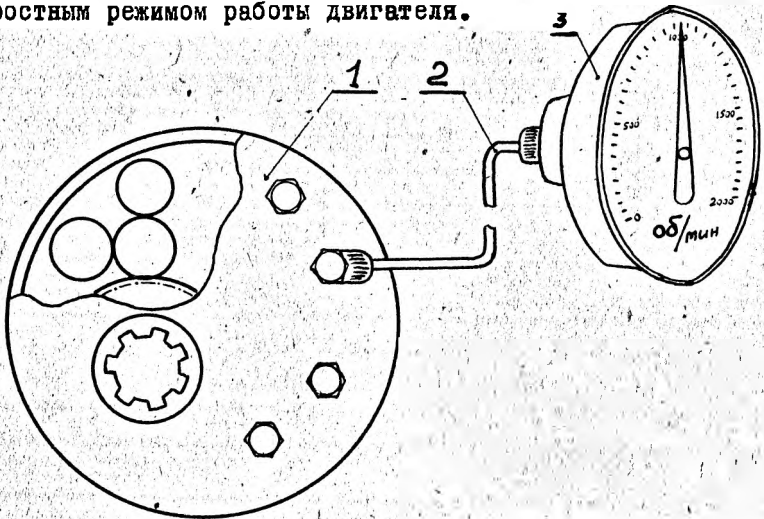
Схема устройства для замера числа оборотов коленчатого вала двигателя: 1-редуктор, 2-гибкий валик, 3-указатель числа оборотов.
